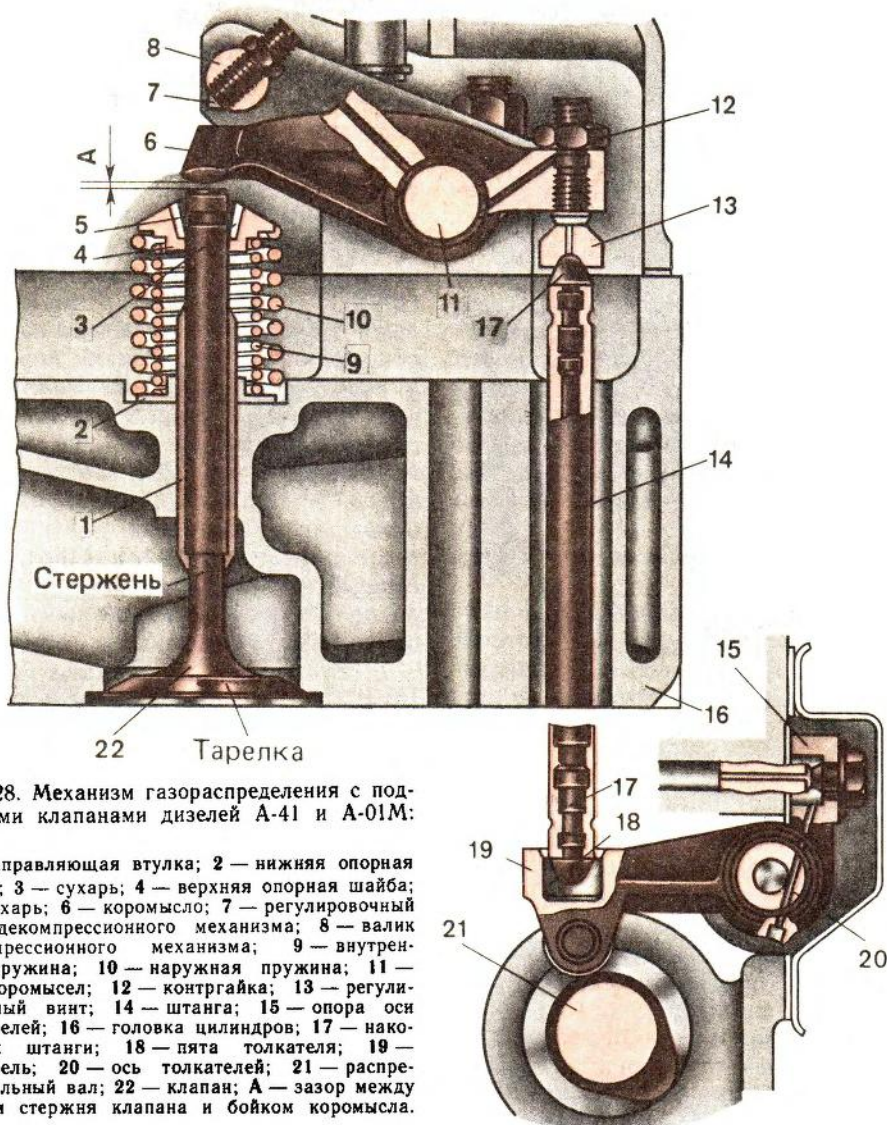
Механизм газораспределения с подвесными клапанами дизелей А-41 и А-01М:
